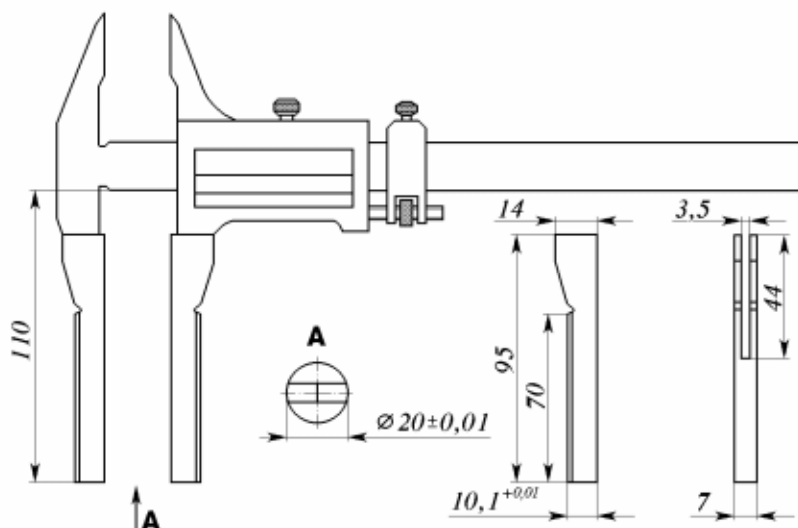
Штангенциркуль для замера натяга манжеты цилиндра подвески
